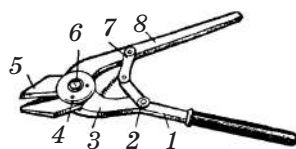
Малогабаритні силові ножиці: 1 — рукоятка; 2 — шарнір; 3 — важіль; 4 — диск; 5 — ніж; 6 — гвинт; 7 — двошарнірний ланцюг; 8 — рукоятка для закріплення в лецатах
